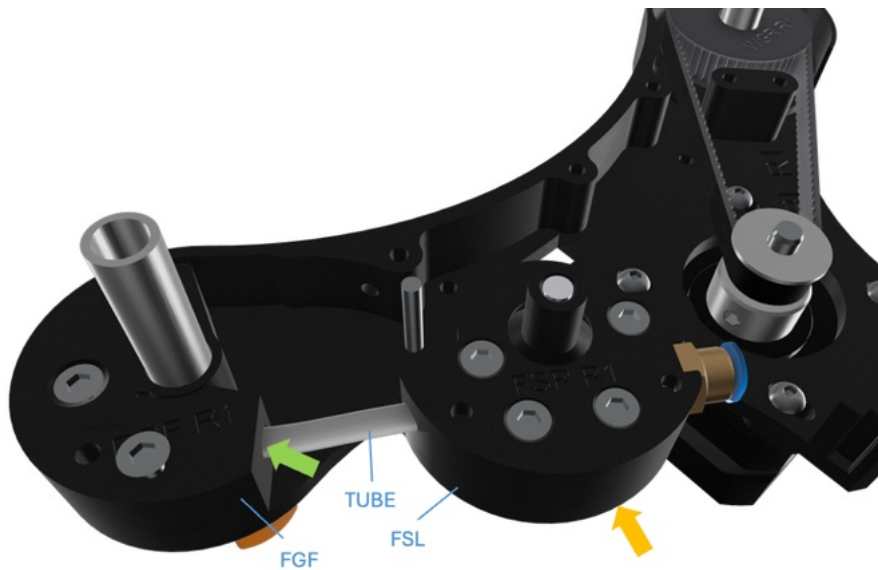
Rewinder-Chassis Montageschritt 19.
